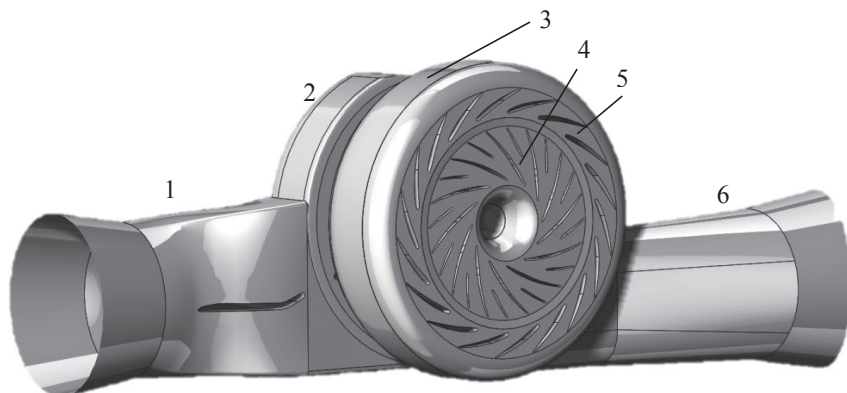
Трехмерная модель одноступенчатого центробежного компрессора:
